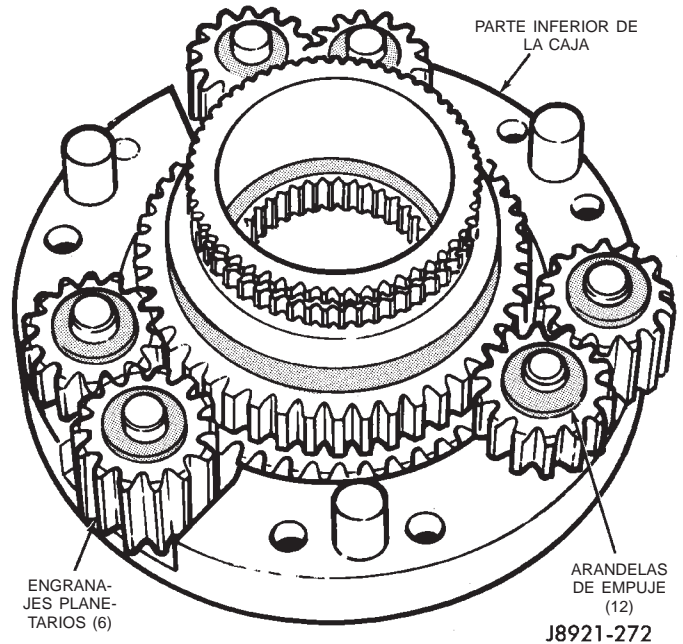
Desmontaje de engranajes planetarios y arandelas de empuje
